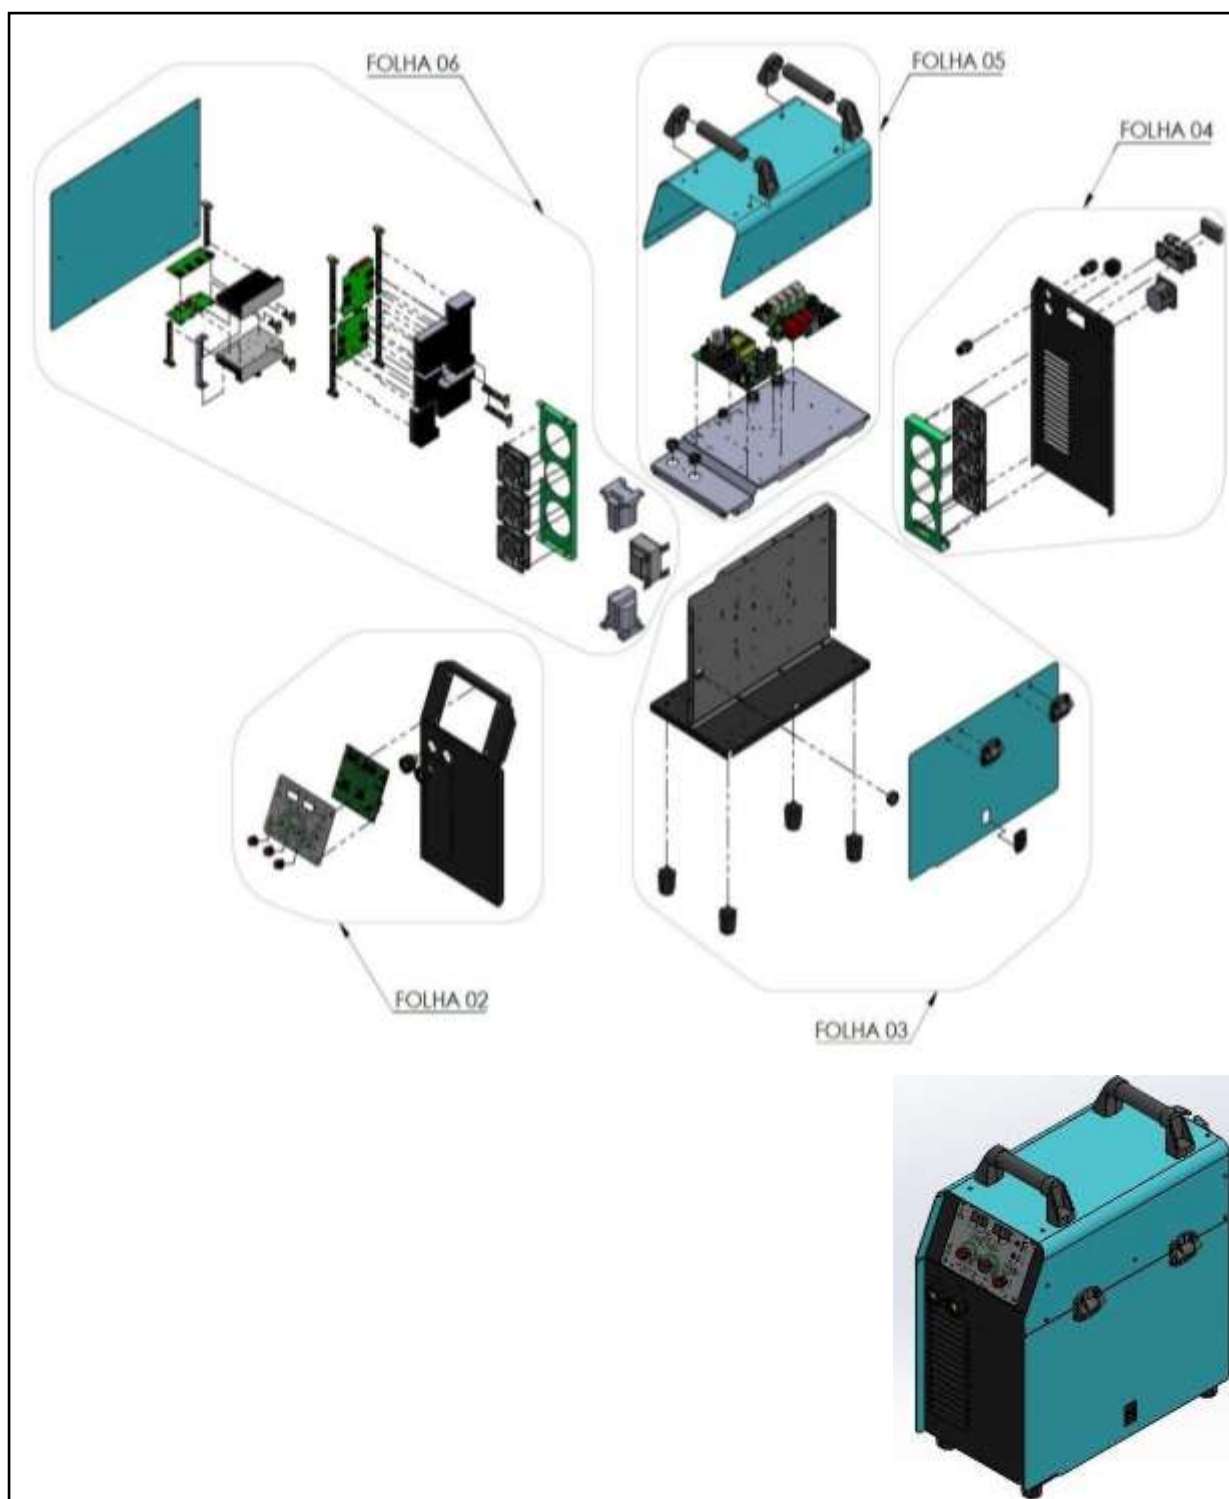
Vista explodida Vulcano Flex MIG 415i.
